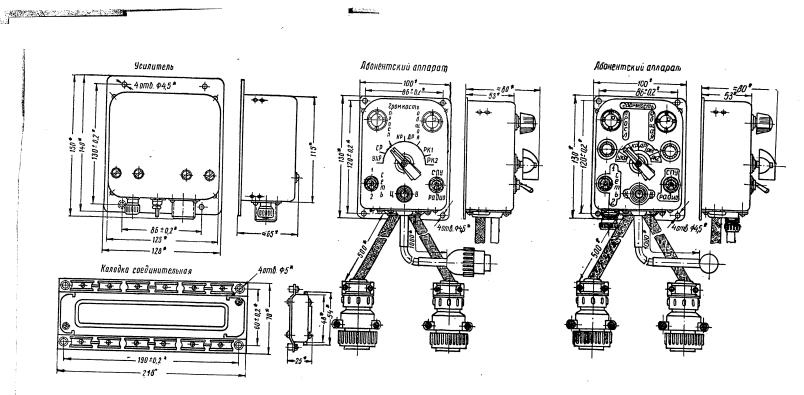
Габаритно-установочные размеры блоков изделия СПУ-7
